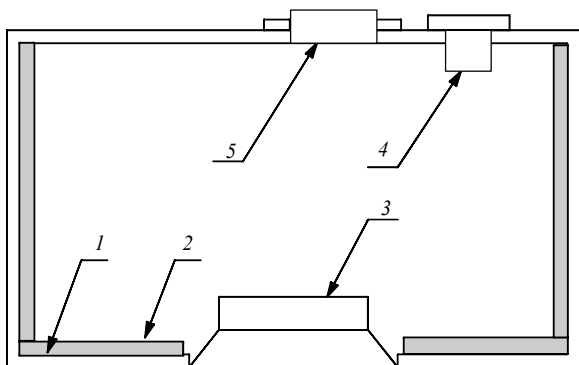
Конструкция акустического блока: 1 – корпус; 2 – демпфер; 3 – электродинамический излучатель; 4 – контрольный микрофон с повторителем; 5 – исследуемый датчик
